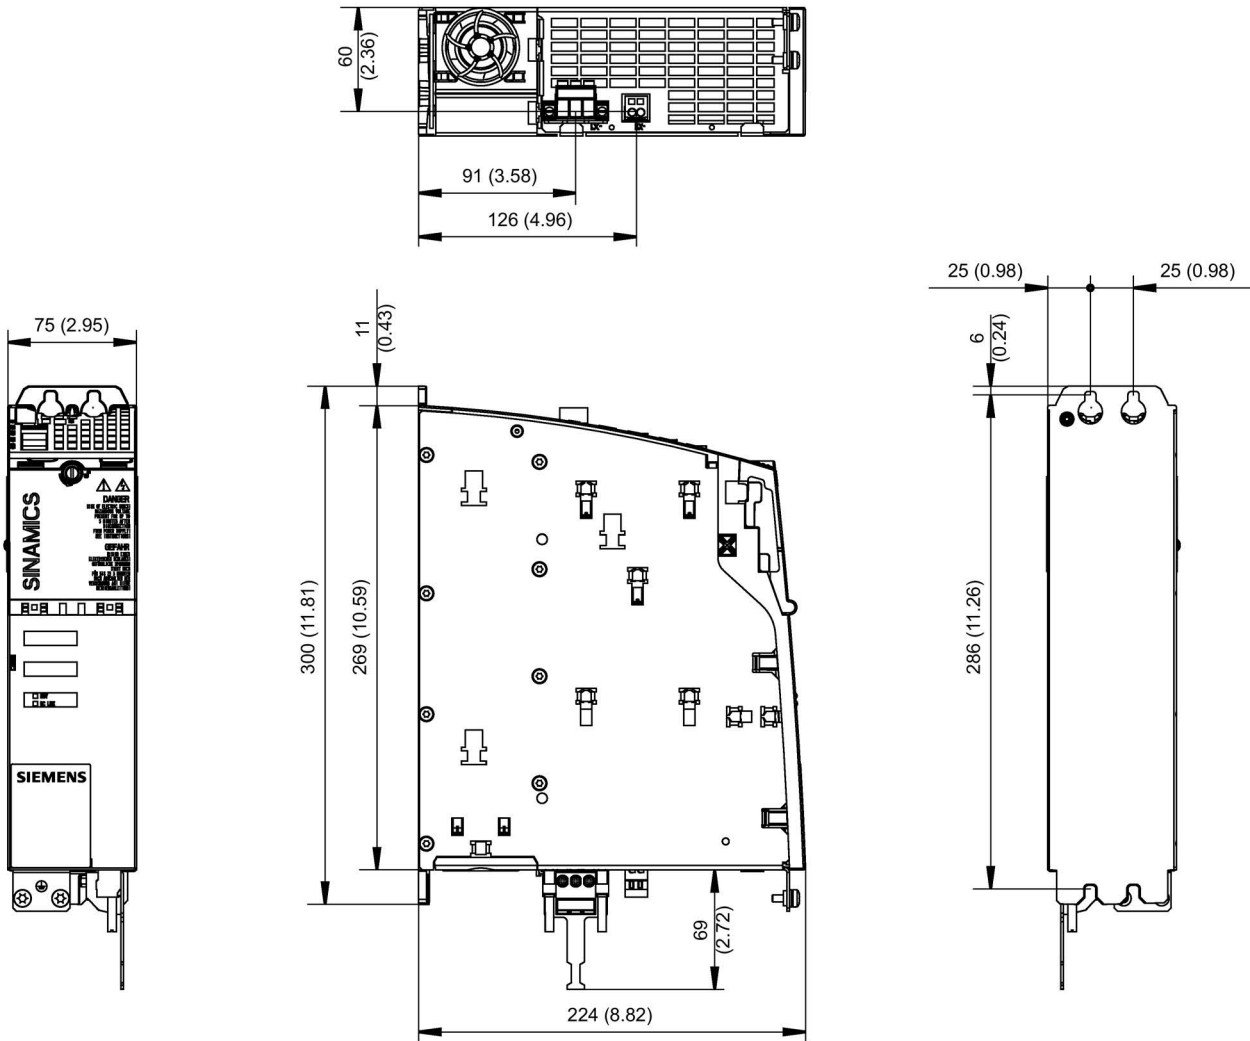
Croquis acotado de Motor Module Booksize Compact de 18 A, todas las medidas en mm y (pulgadas)
